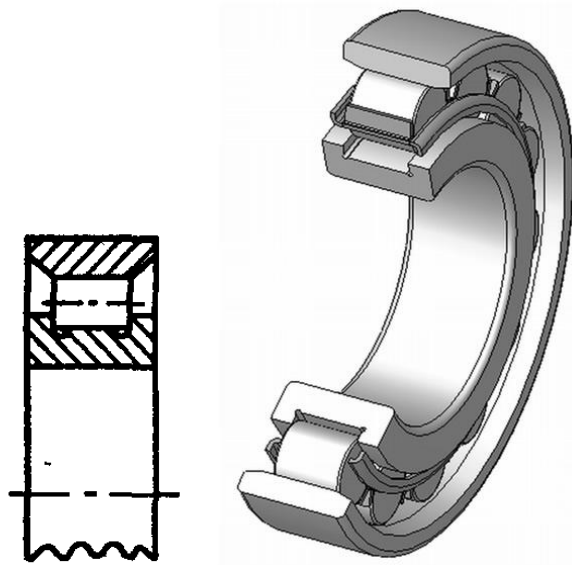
Роликовий радіальний однорядний розбірний з циліндричними роликами
